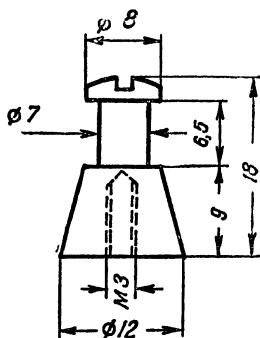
Неподвижный ролик из бронзы или латуни. Для лентопротяжного механизма нужно два таких ролика
